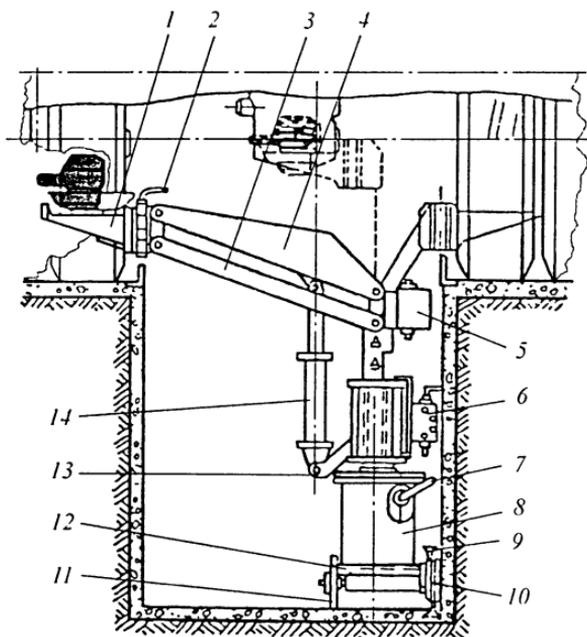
Устройство для замены агрегатов автомобиля: 1 — сменный подхват, 2 — соединительная ручка; 3 — пантограф; 4 — подъемная стрела; 5 — бачок; 6 — золотник; 7 — воздухораспределительный кран; 8 — пневмоцилиндр; 9 — двутавровая балка; 10 — металлическое колесо; 11 — обрешиненное колесо; 12 — тележка; 13 — кронштейн, 14 — гидроцилиндр
